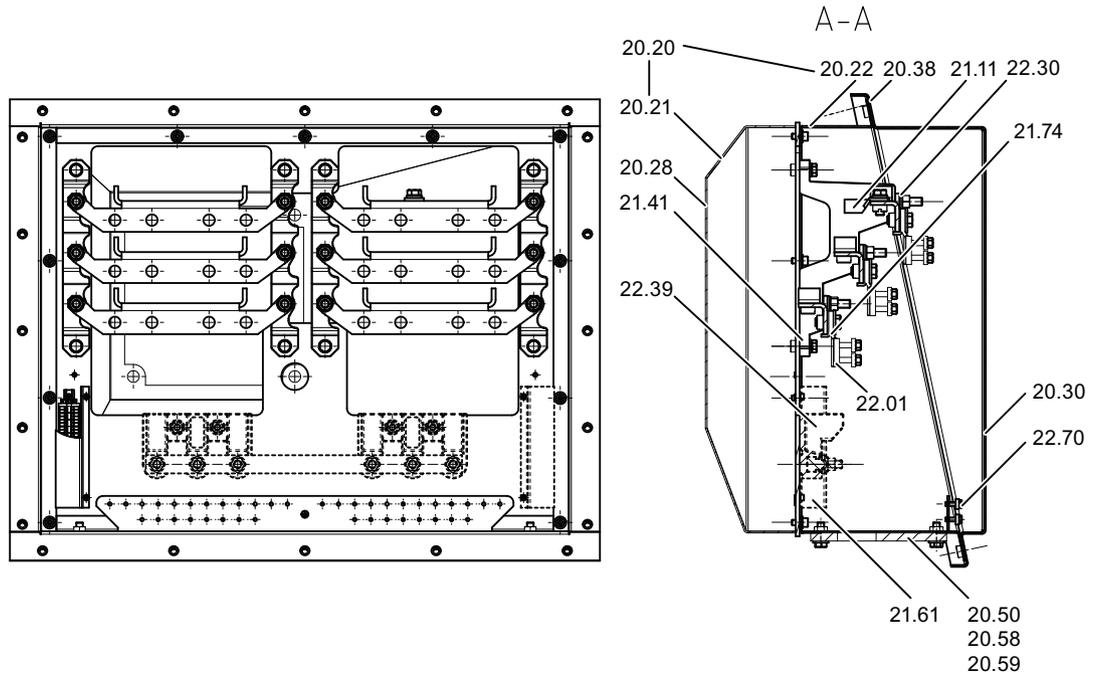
Hauptklemmenkasten 1XB7750 mit Standardkabeinführung
